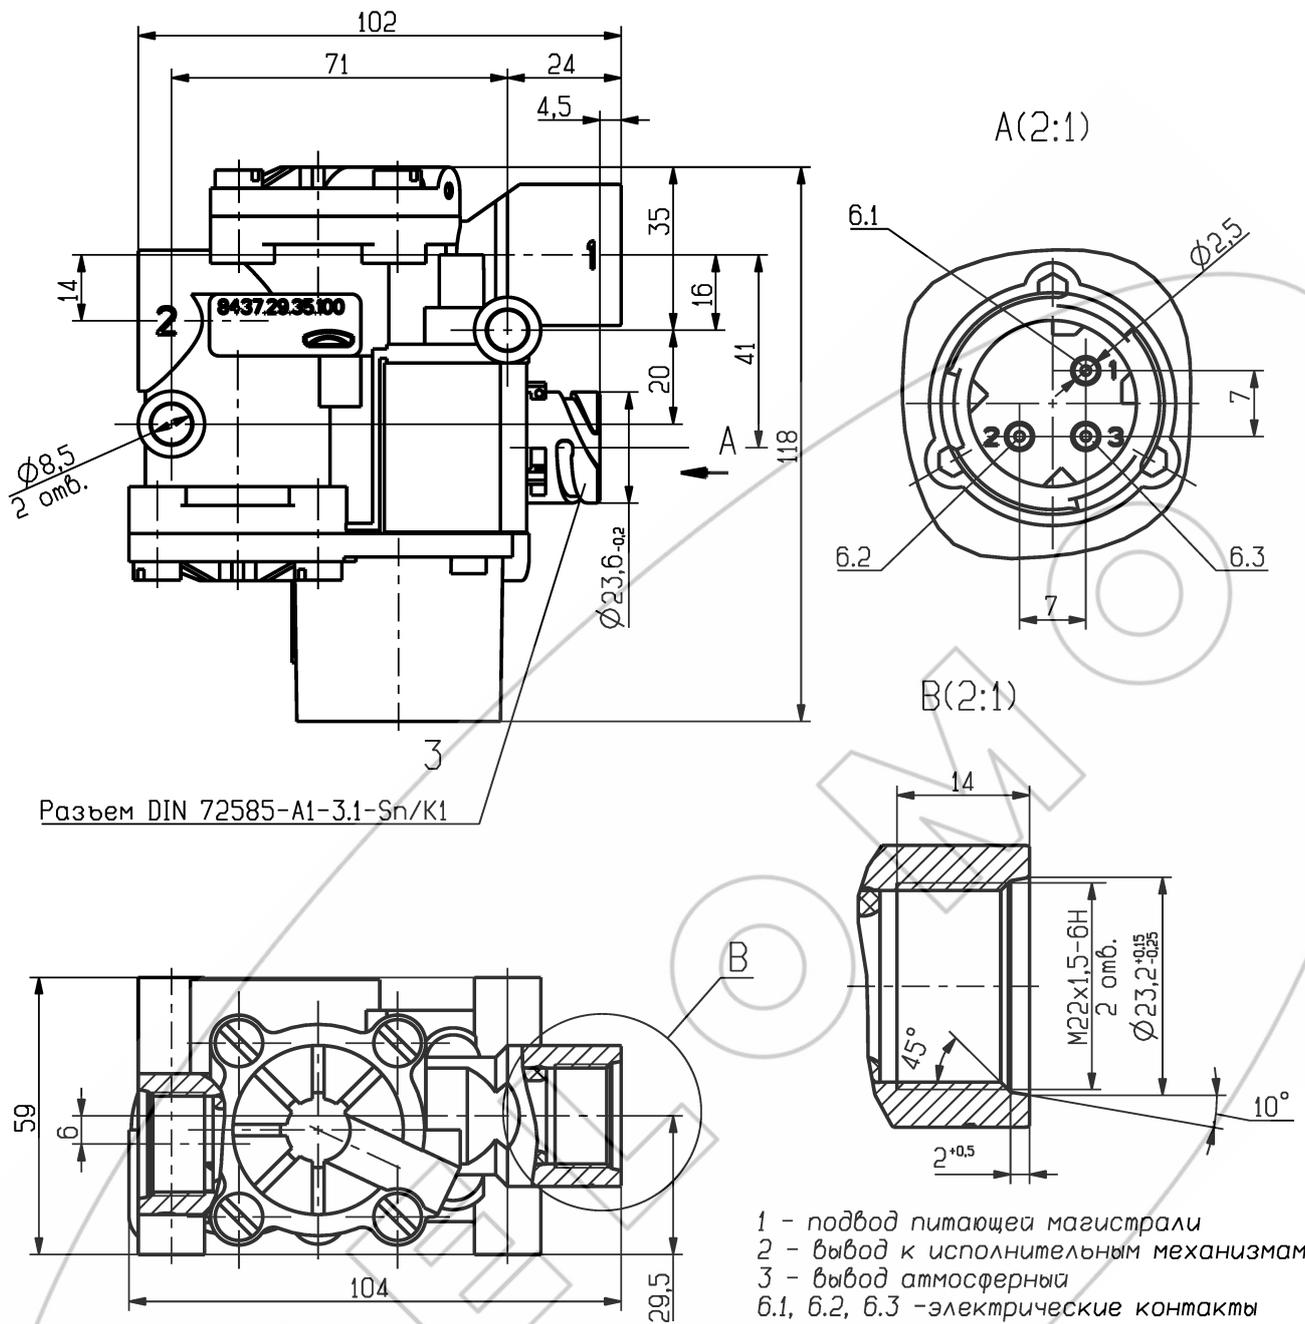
Габаритные и присоединительные размеры модулятора
